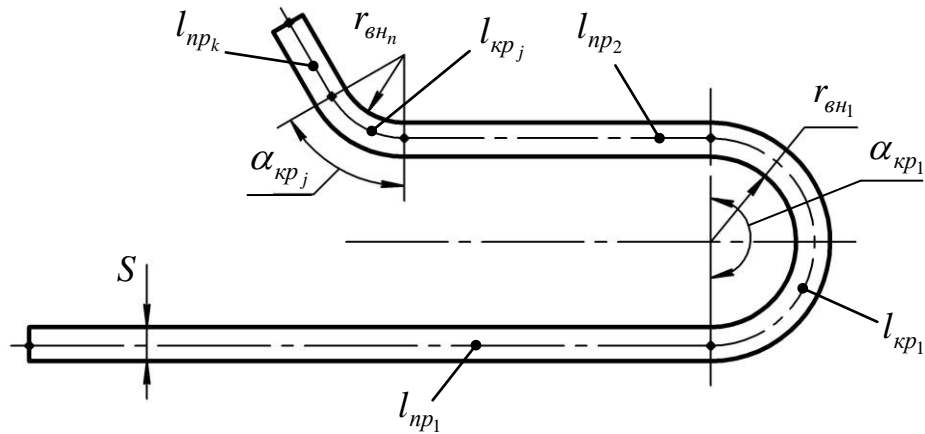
Схема розрахунку довжини заготовки для гнуття
